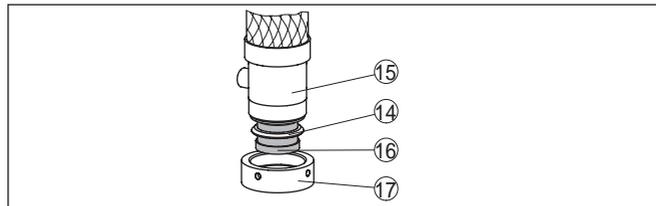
Montaje de la refrigeración de escintilador - parte inferior
